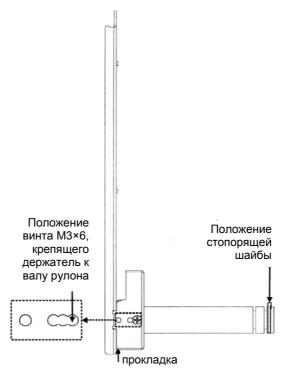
Установка рулона шириной 82,5 мм (вид рулонодержателя сверху)
